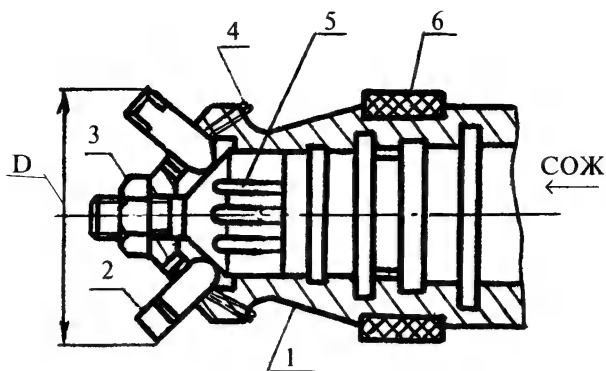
Многорезцовая расточная головка с расположением резцов по окружности: 1 - корпус головки, 2 - резец, 3 - винтовая пара, 4 - винт, 5 - опорный конус, 6 - шпонка направляющая
